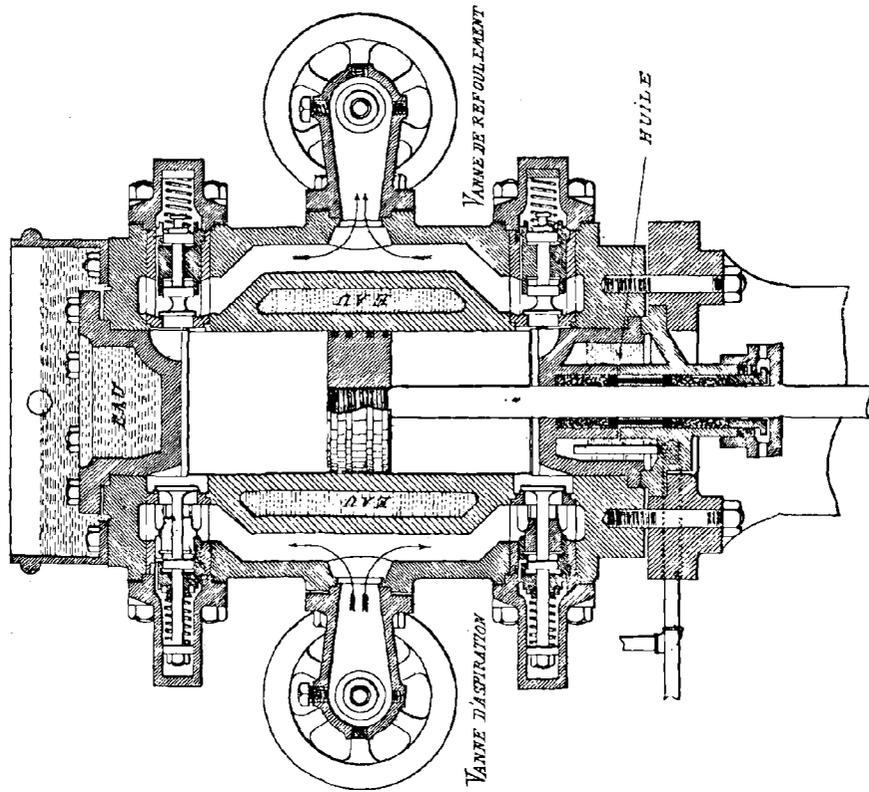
Compresseur de la Buffalo Refrigerating Machine C.
